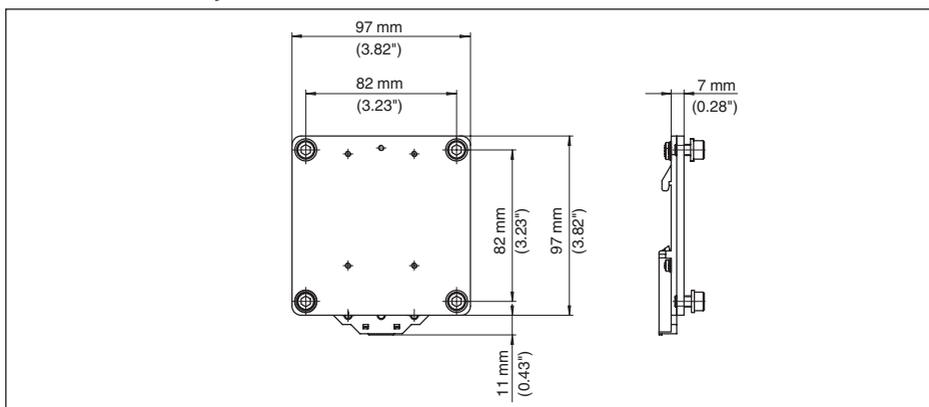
Placa adaptadora para montaje en regletas de montaje de VEGABOX 03
